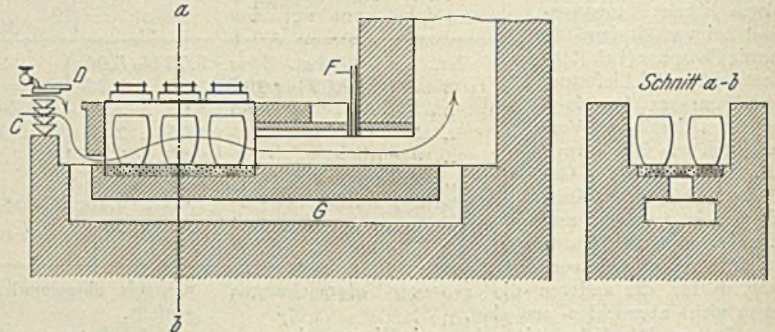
Tiegelofen der Sivy Steel Casting Co. in Milwaukee.
